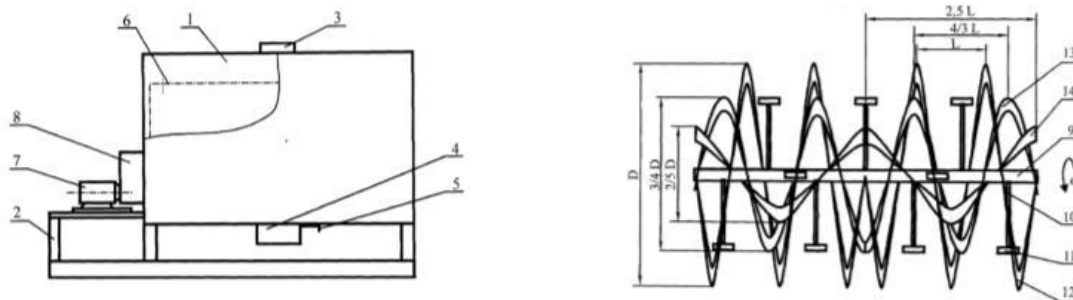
Змішувач за патентом № 2488434: а – конструкційна схема; б – комбінований шнек; 1 – бункер; 2 – рама; 3, 4 – завантажувальний і розвантажувальний патрубки; 5 – заслінка; 6 – комбінований шнек; 7 – двигун; 8 – редуктор; 9 – вал; 10 – стрижні; 11 – елементи стрічкової спіралі; 12 – зовнішній стрічковий шнек; 13 – середній стрічковий шнек; 14 – внутрішній стрічковий шнек.
